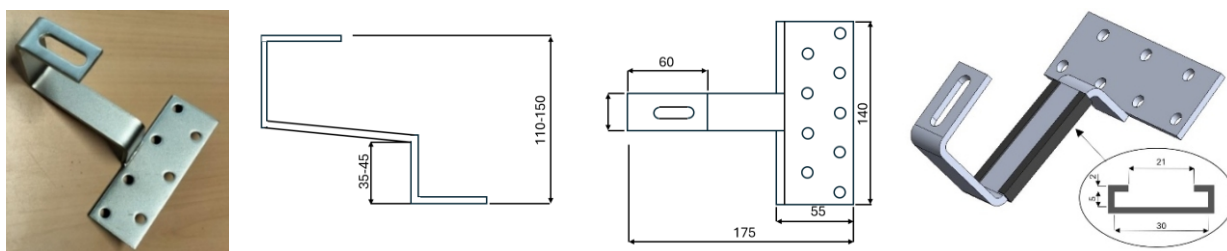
Pattes de fixation toitures tuiles à emboîtement
